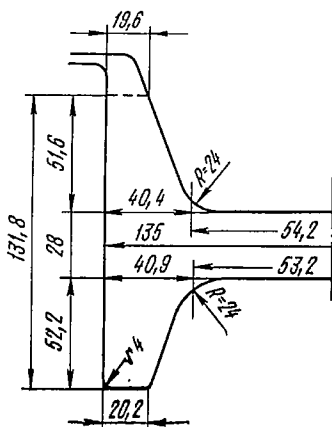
Конструкция и размеры седьмого калибра (считая от чистового)
